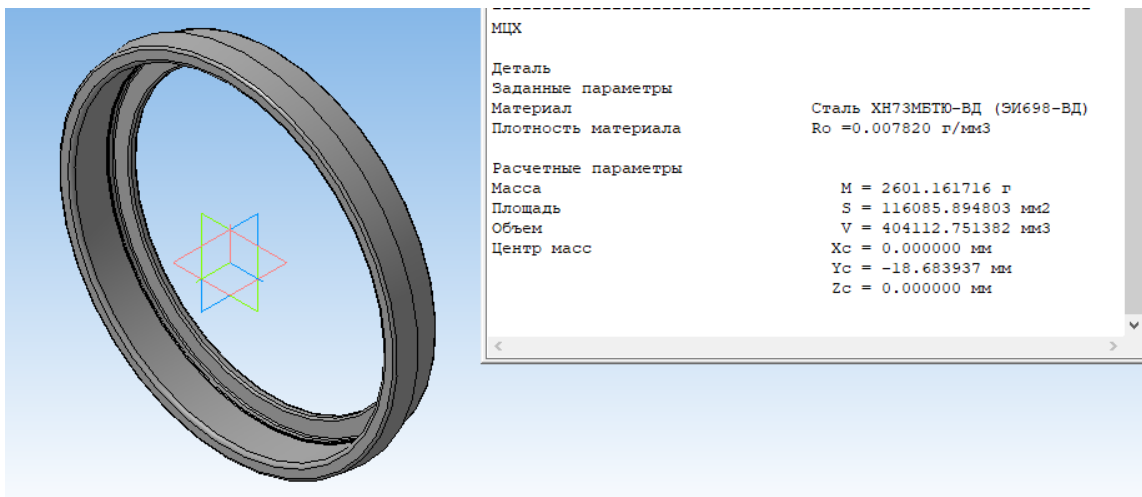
3D модель штампованої заготовки на КГШП
